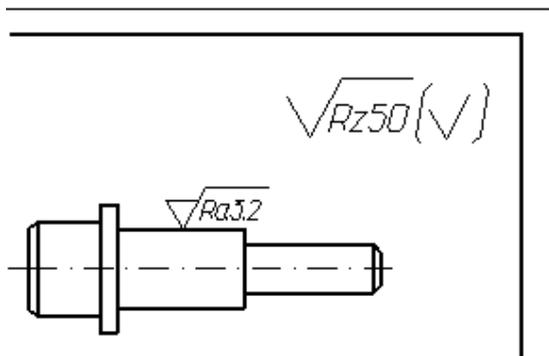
Указание шероховатости одинаковой для части поверхностей изделия
